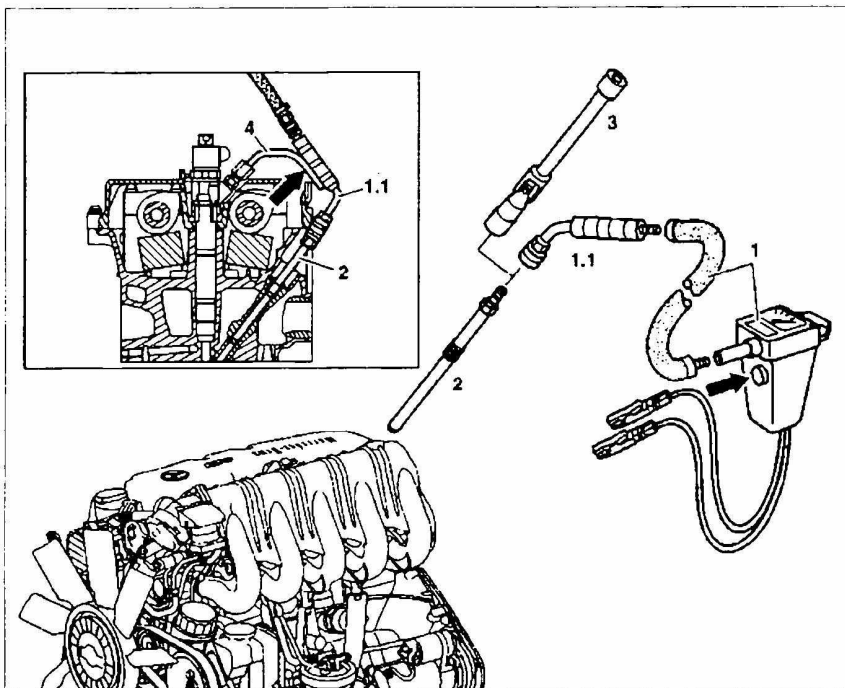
б. Проверка компрессии (на двигателях 612.981):
